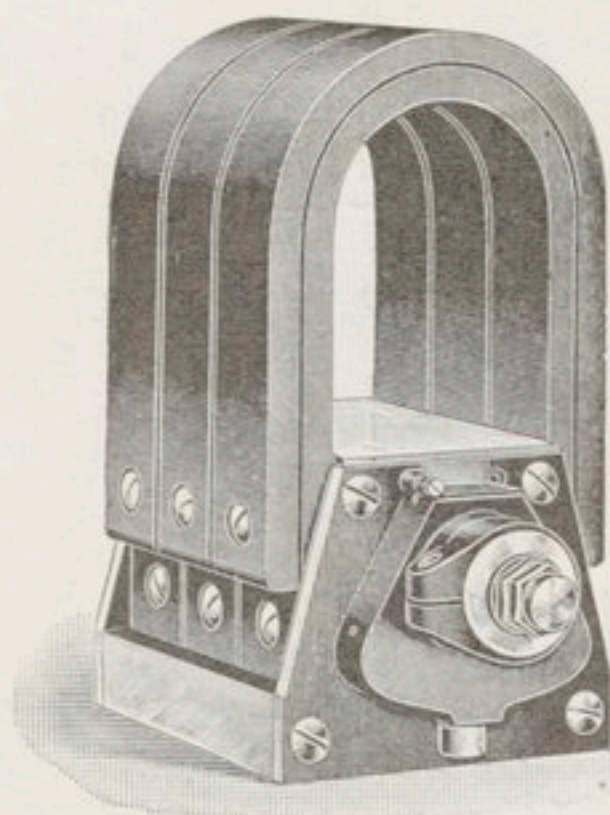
Magnéto Bosch à rupture. Vue d'ensemble.
